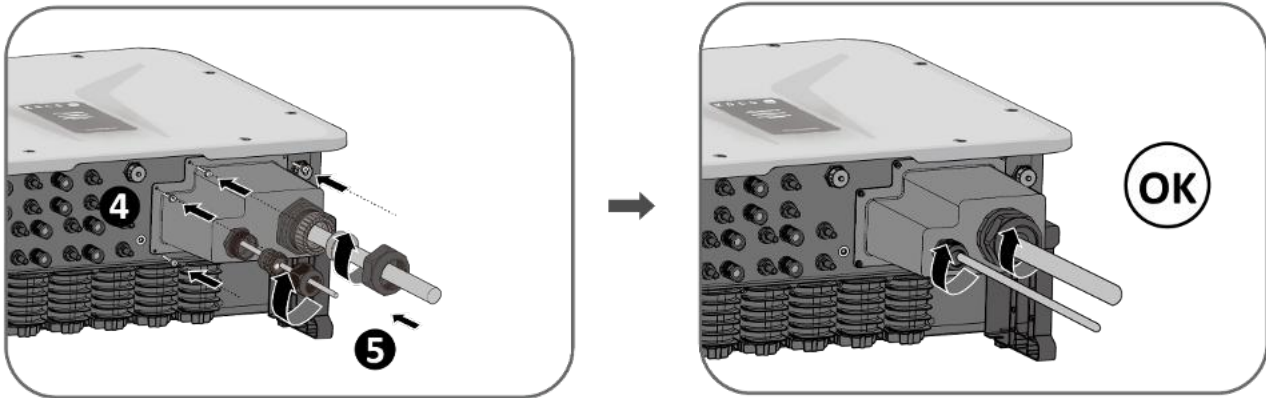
AC/COM-Abdeckung aufsetzen und Muttern festschrauben.
